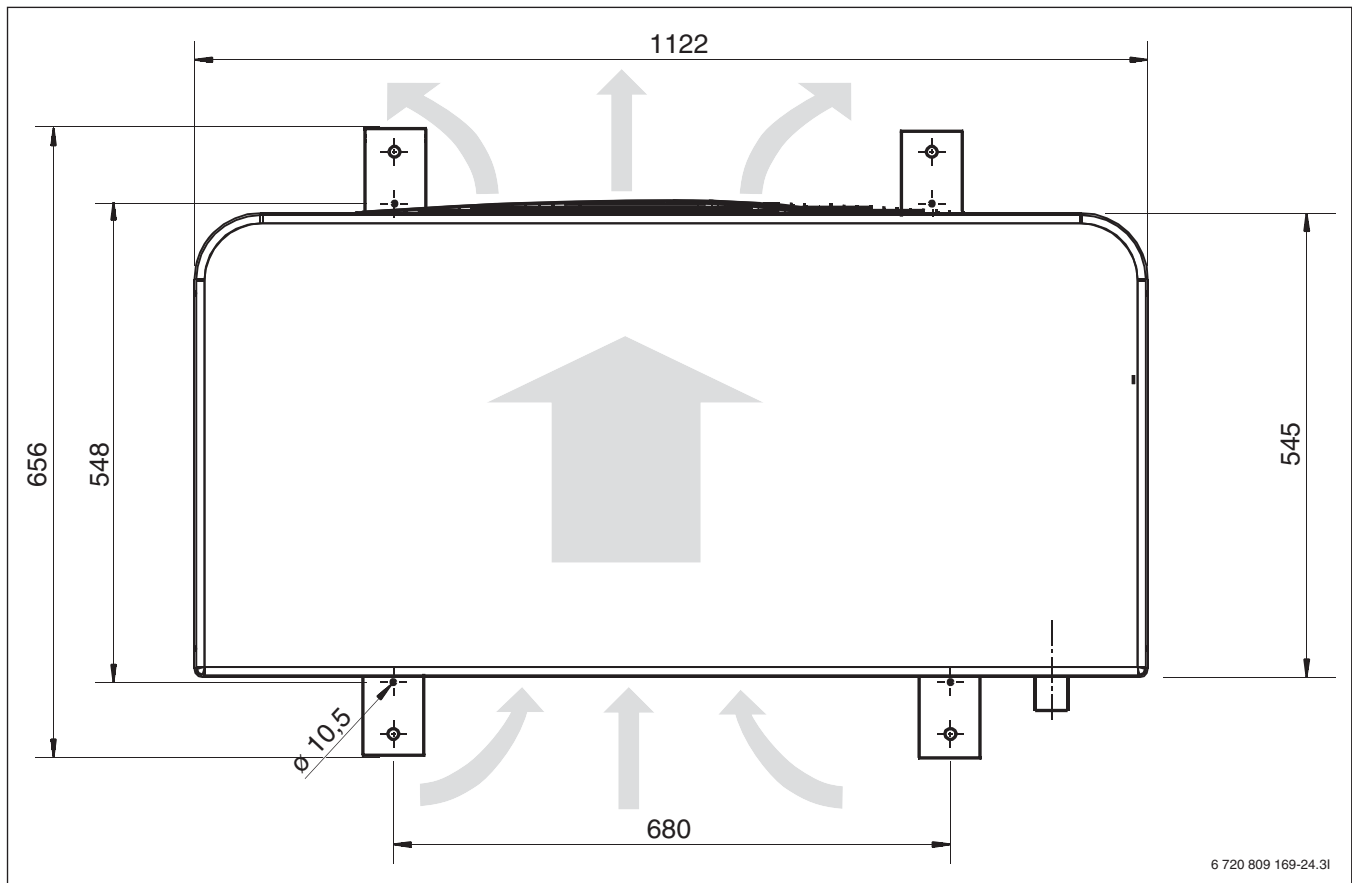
Abmessungen der SAO 110-2 / SAO 140-2, Draufsicht
